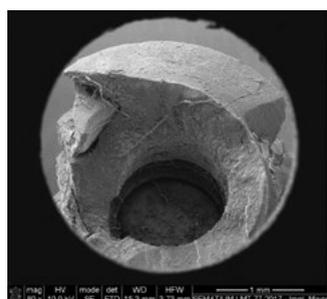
Vista do implante maior – parte fraturada, outra vista.
